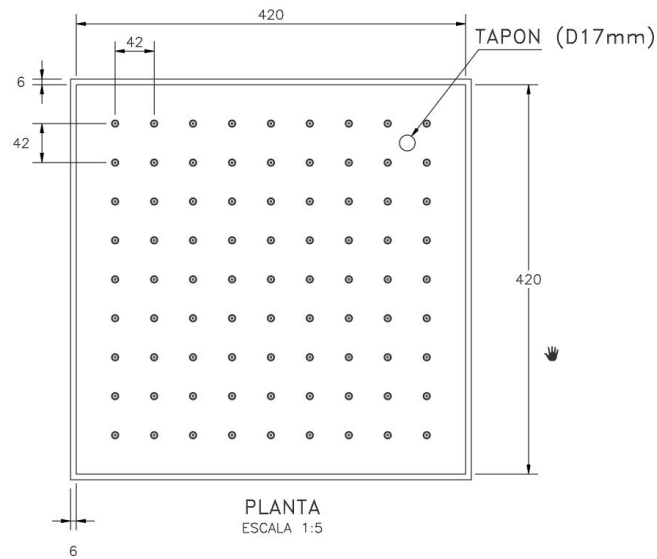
Vista de planta inferior de la regadera (Elaboración propia).
